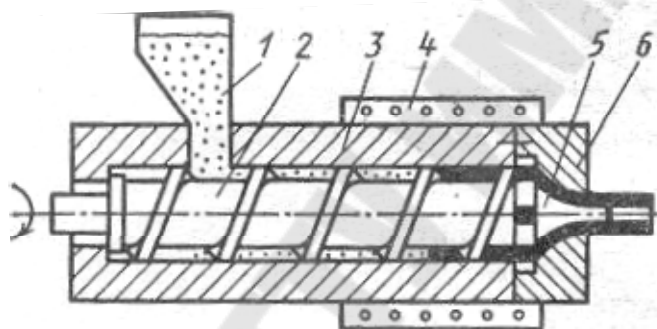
Схема экструдера для непрерывного выдавливания профиля: 1 – бункер; 2 – шнек; 3 – обогреваемый цилиндр; 4 – червяк; 5 – оправка с радиальными каналами; 6 – профилирующая головка
